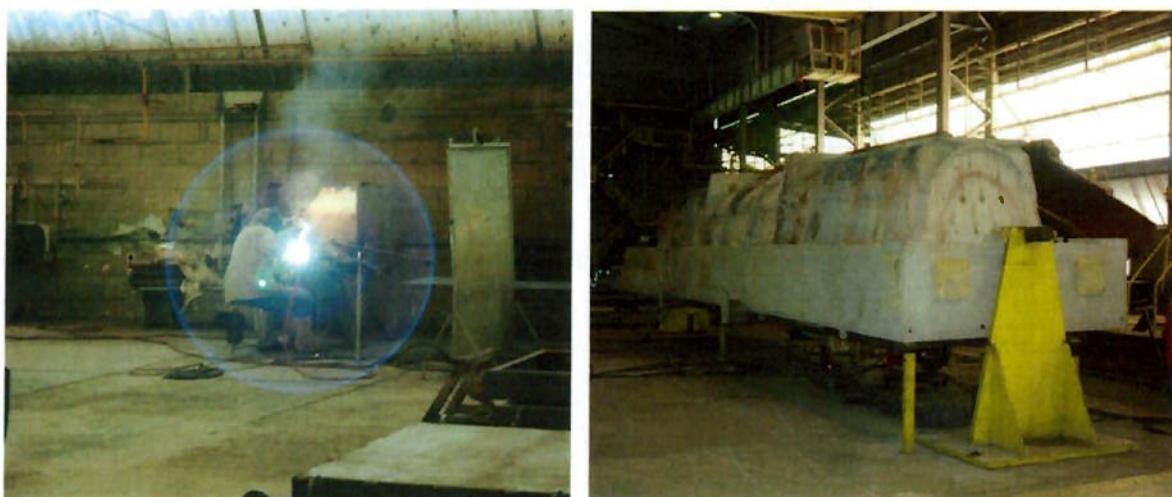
Exemplo do Setor de Montagem e Solda – Área Leve.
